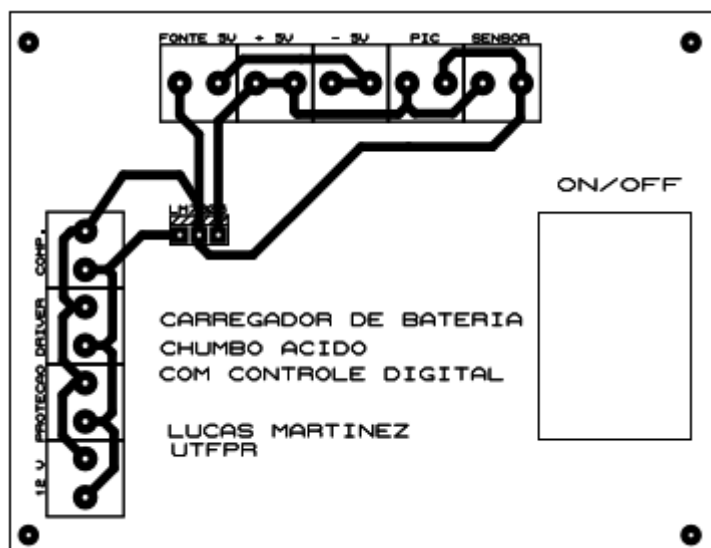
Layout da Placa de Circuito Impresso da Fonte Auxiliar
